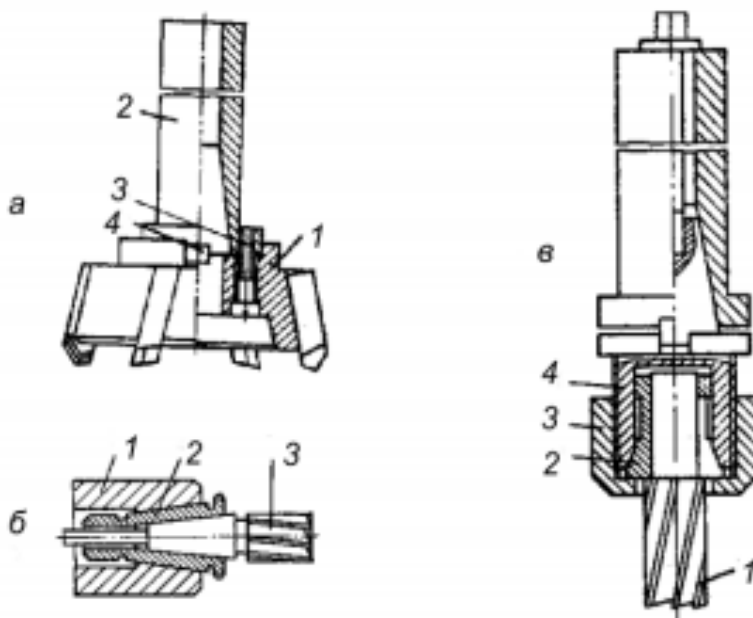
Схеми установки і закріплення фрез на верстатах
